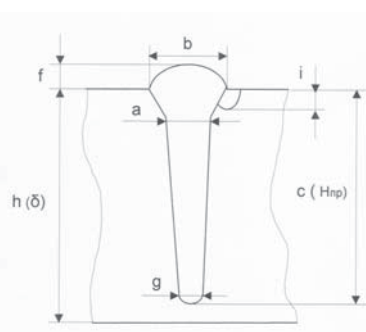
Сварной шов без сквозного проплавления: $h(\delta)$ — толщина свариваемой пластины; $c(H_{np})$ — глубина проплавления; b — ширина лицевого валика сварного шва; a — наибольшая ширина средней части зоны проплавления; g — наименьшая ширина средней части зоны проплавления; f — усиление лицевого валика сварного шва; i — величина подреза с лицевой стороны шва
